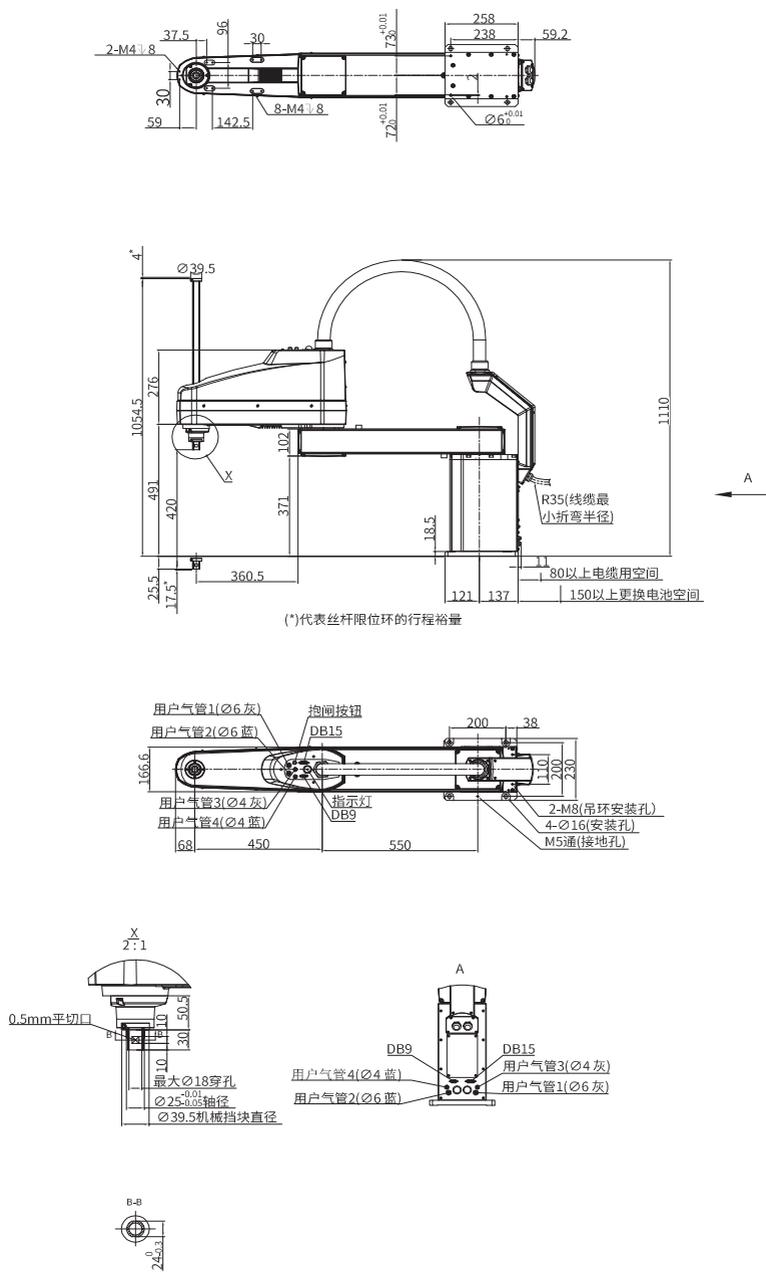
IRB111-20-100Z42TS3 安装尺寸
